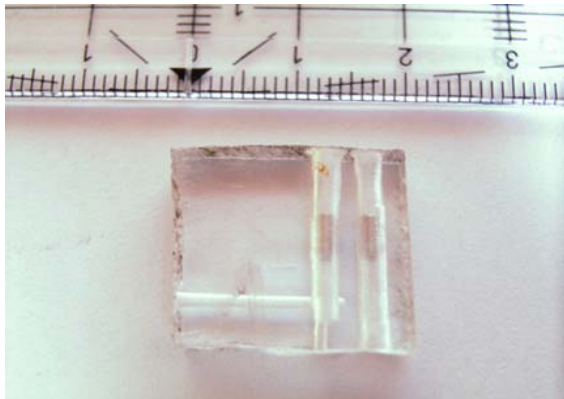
Die Mikropumpe mit richtiger Bohrtechnik.
